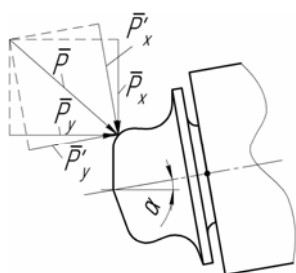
Розкладання повного зусилля, що діє на валок вздовж осі обертання валка та вздовж осі обертання заготовки
